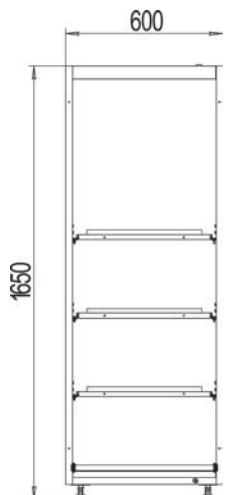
Габаритный чертеж стеллажа аккумуляторного 1650x600x600
